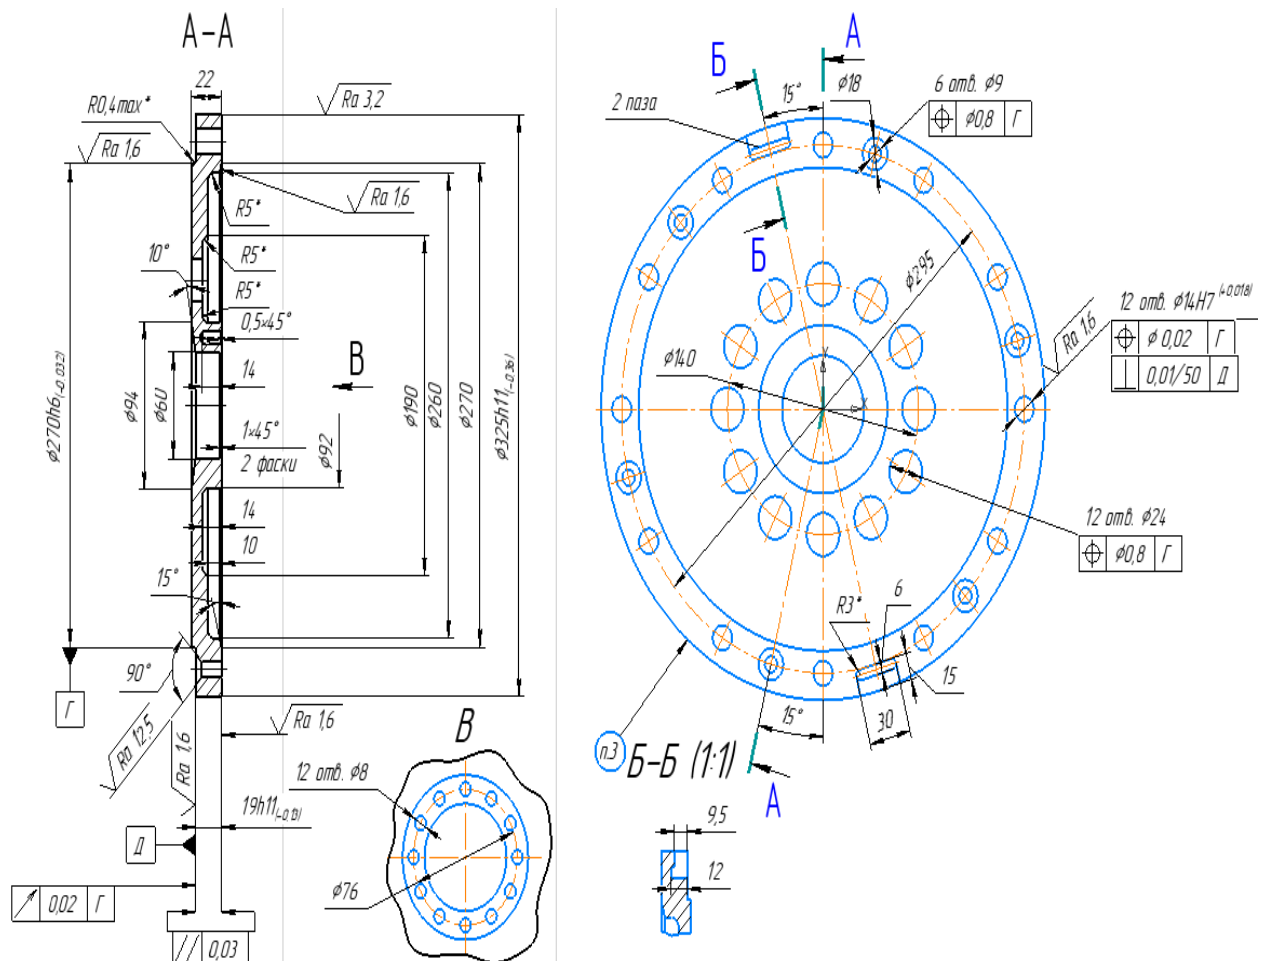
Оброблювані поверхні деталі «Диск направляючий»
